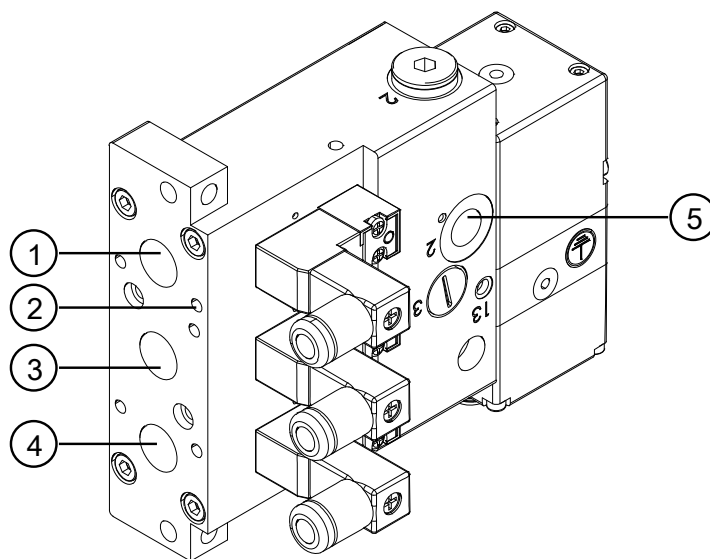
Gasanschluss 2- und 3-Gas-Variante mit oder ohne Filter
